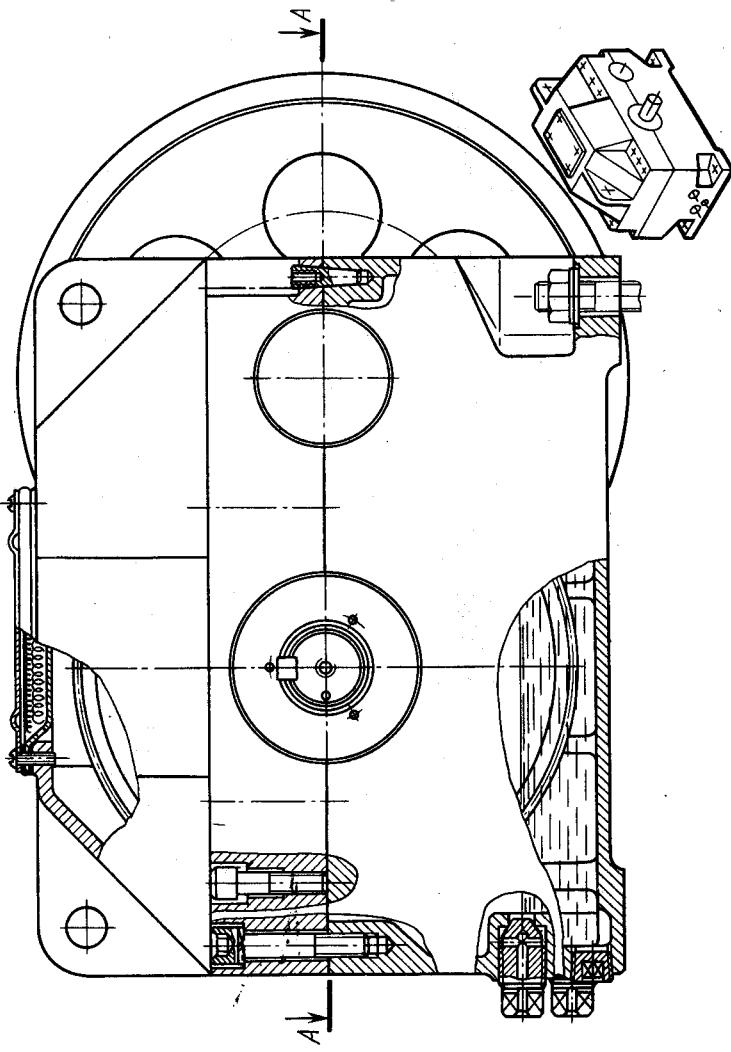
Редуктор цилиндрический одноступенчатый горизонтальный
